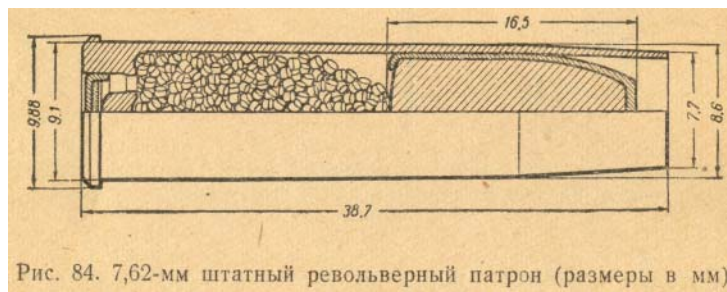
7,62-мм штатный револьверный патрон (размеры в мм)
